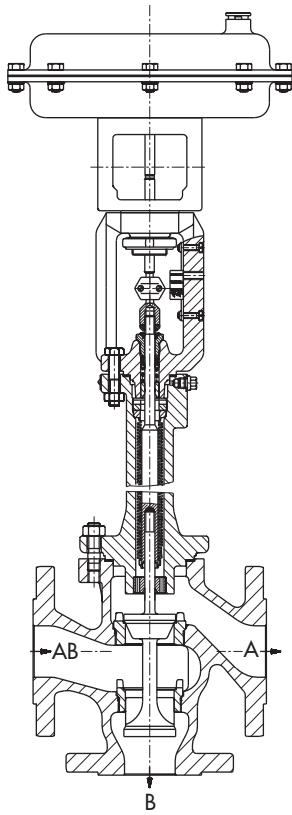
· Пневматический регулирующий клапан тип 3244-7 с трехходовым вентилем тип 3244 (расположение конуса для работы в режиме распределителя), дополнительным металлокомпенсаторным уплотнением и сервоприводом тип 3277.
